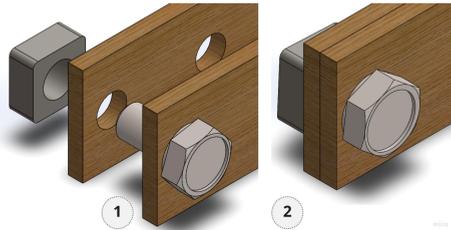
Fixação paralela - rendering. Fonte: A autora.
